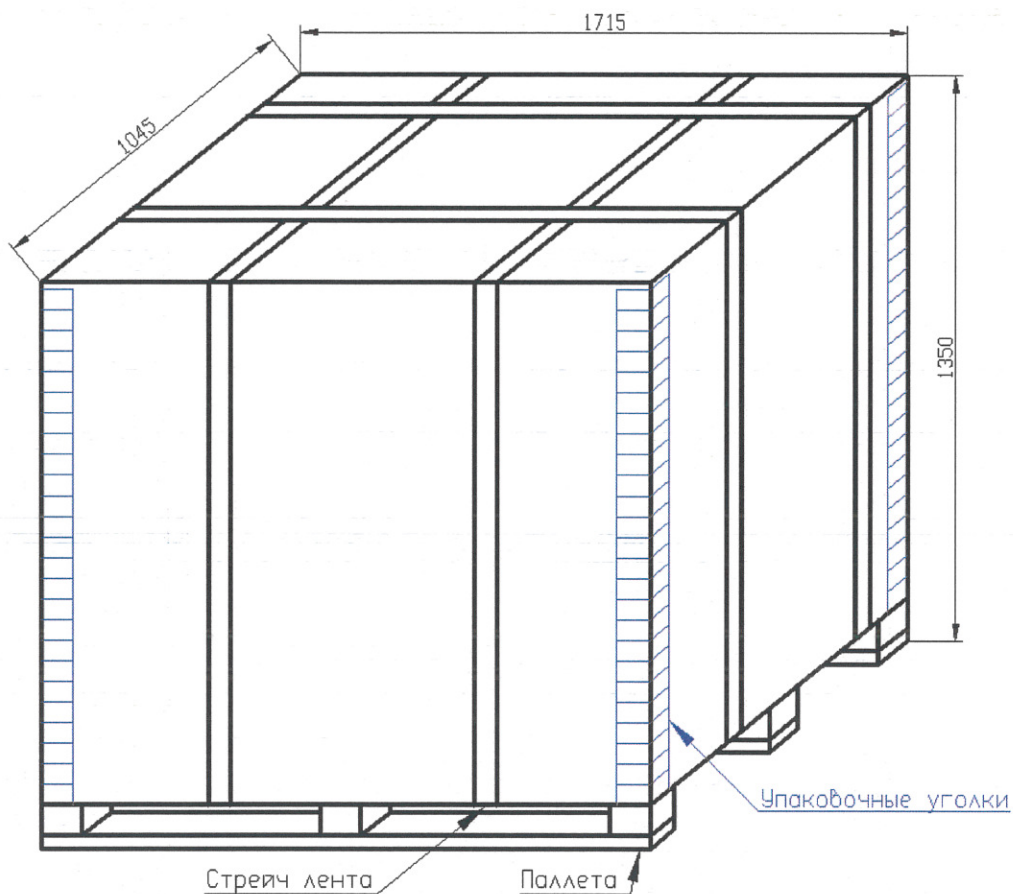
Габаритные размеры упаковки с ФЭМ
